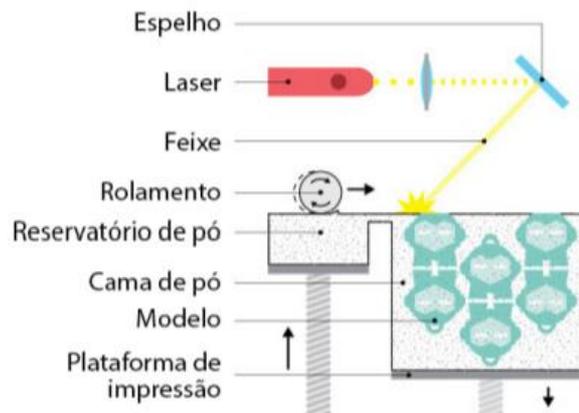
Desenho esquemático do processo de prototipagem rápida por SLS[37].
